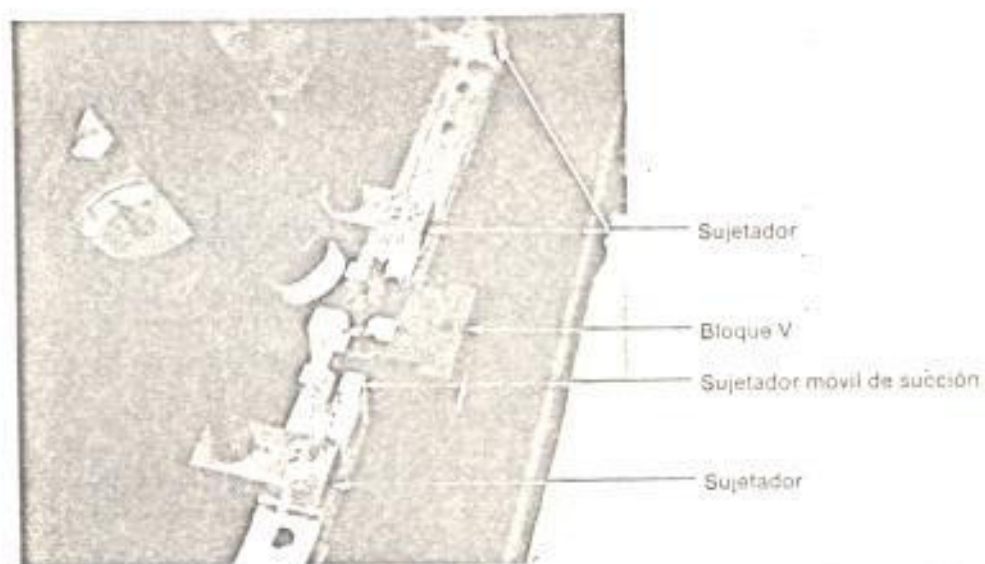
EQUIPO DE EMPALME POR EL METODO DE SOLDADURA
